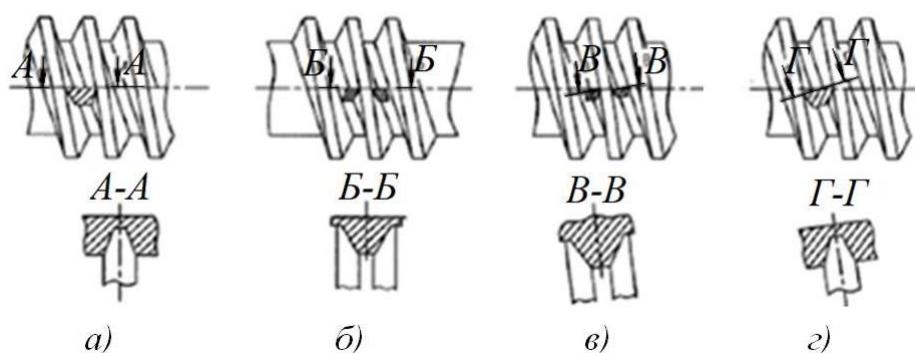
Способи нарізування зубців черв'яка [35]
